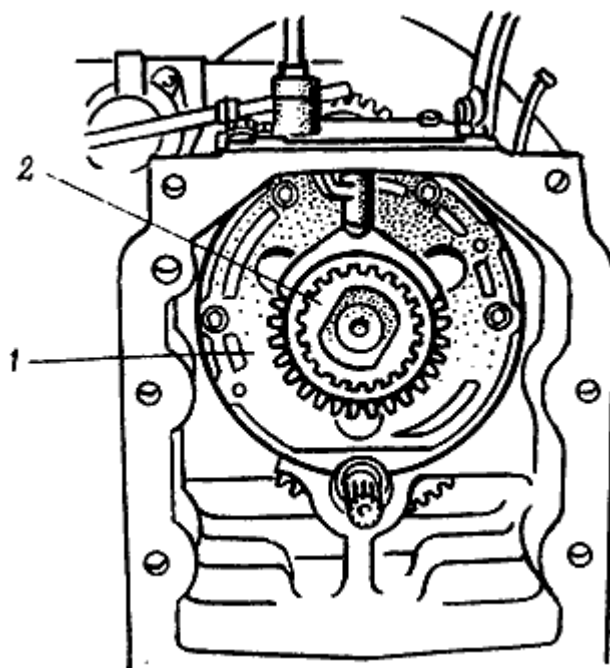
Снятие механизма управления понижающим редуктором и зубчатой муфтой:
